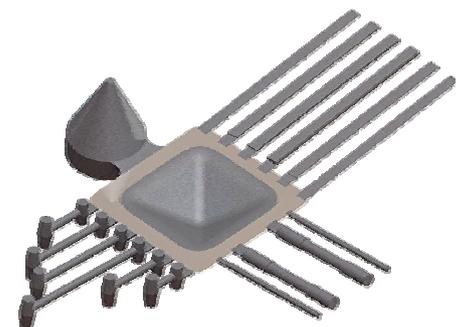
Multifunktionskokille: Virtueller Abguss mit Lage der einzelnen Prüfkokillen für Fließlänge, Zugstäbe, Warmrisseigung und Lunkerneigung (Tatur).
